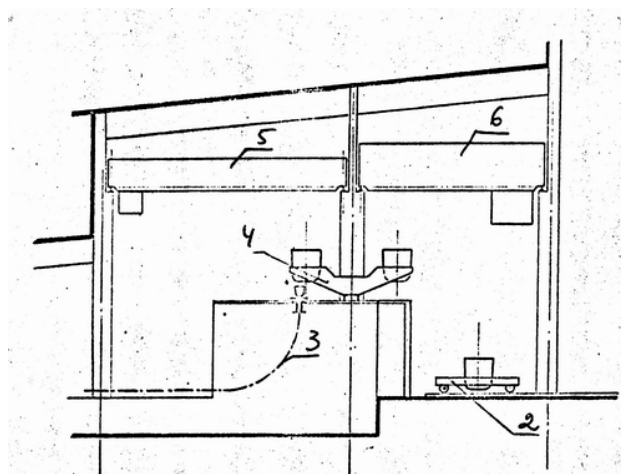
Линейное расположение МНЛЗ с разливкой стали с поворотных стенов. Разрез: 1 — конвертер, 2 — сталевазная тележка, 3 — МНЛЗ, 4 — поворотный сталеразливочный стенд, 5 — мостовой кран, 6 — мостовой разливочный кран
